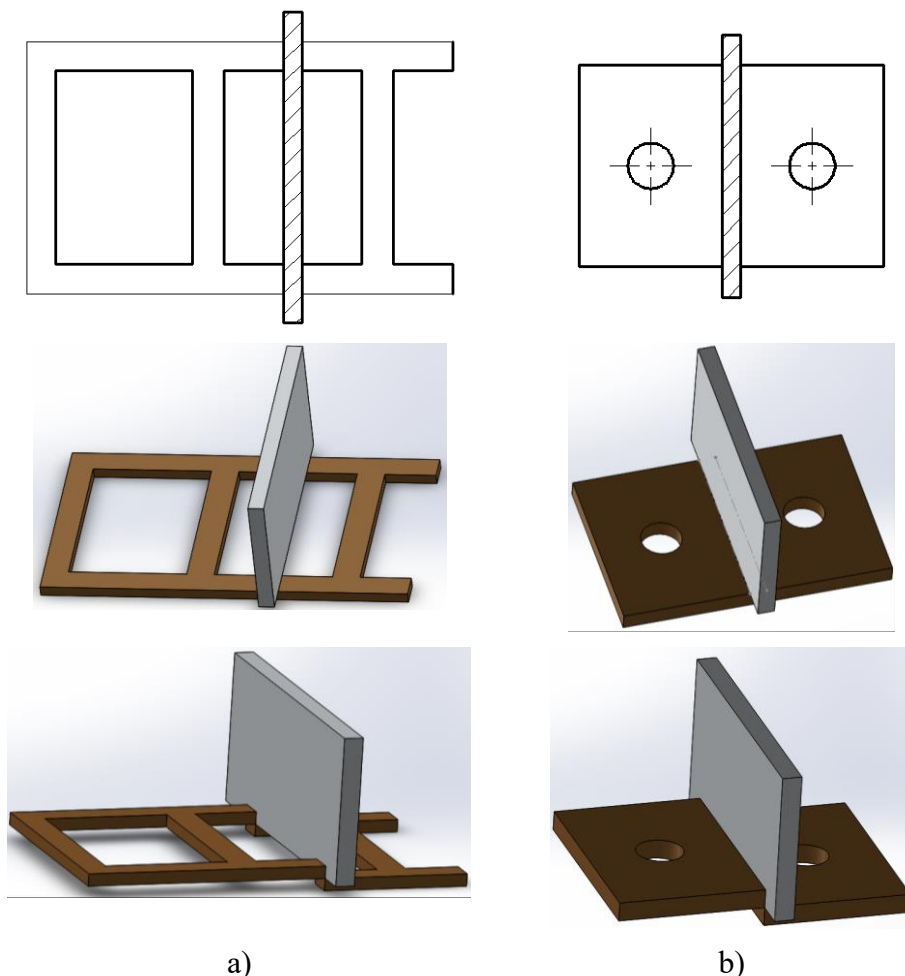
Retezare: a) retezare deșeu, b) retezare piesă
